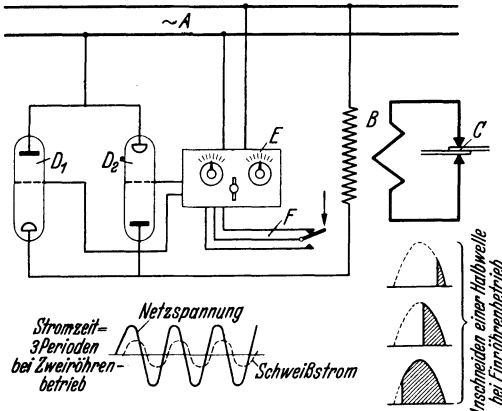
Stromrichtersteuerung für Punkt- und Nahtschweißung.
